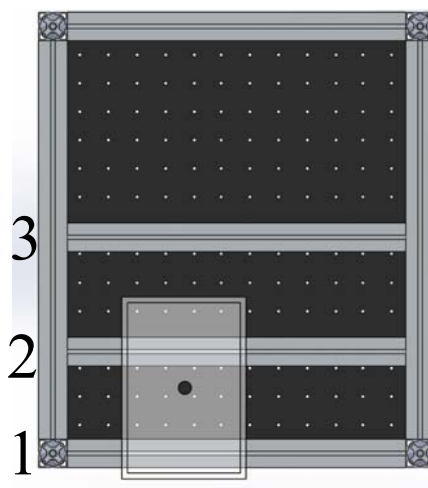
Vista superior com a disposição dos elementos transversais para suporte da bancada.
